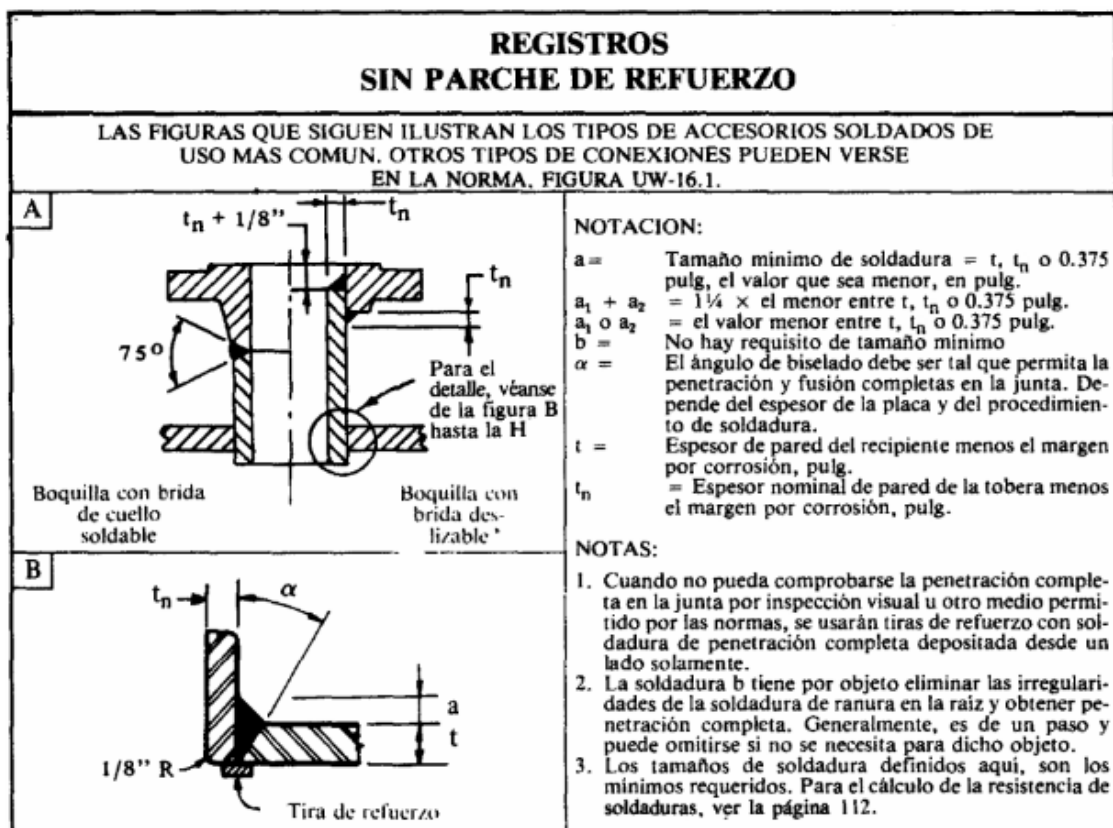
Soldadura de tubuladura (con brida de cuello soldable) sin parche de refuerzo.
